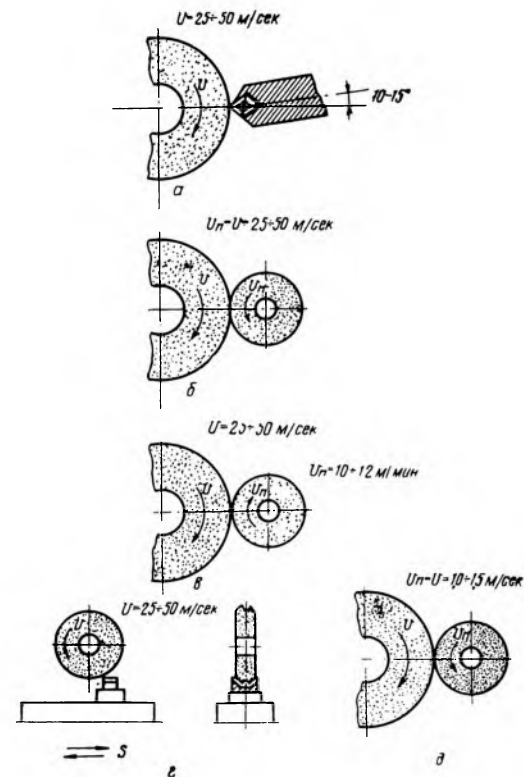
Методы правки шлифовальных кругов: а — обтачиванием; б — обкатыванием; в — шлифованием; г — тангенциальным точением; д — накатыванием
